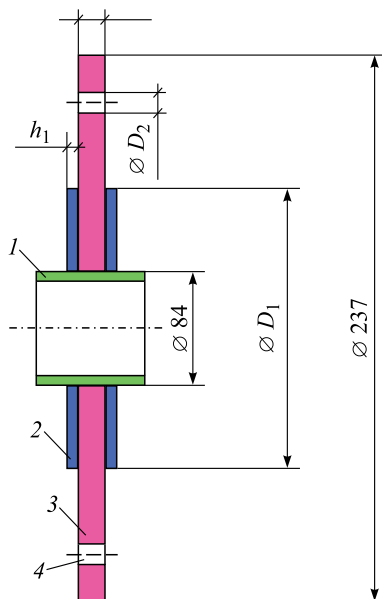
Конструкция переходника, обеспечивающая отсутствие образования при сварке интерметаллидов ниобия: 1 — ниобиевый патрубок; 2 — титановые пластины; 3 — диск из нержавеющей стали; 4 — технологические отверстия
